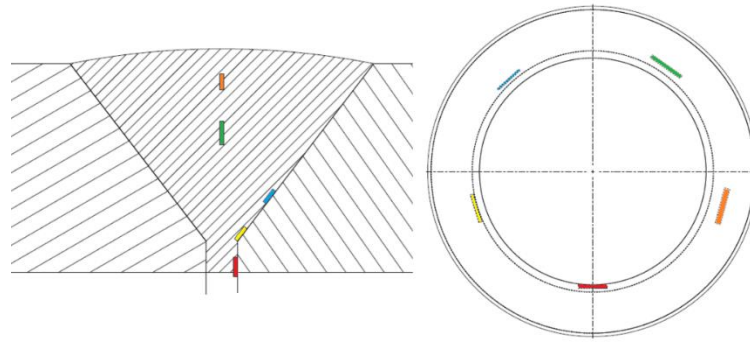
Representação esquemática sobre o posicionamento dos entalhes na soldadura.
